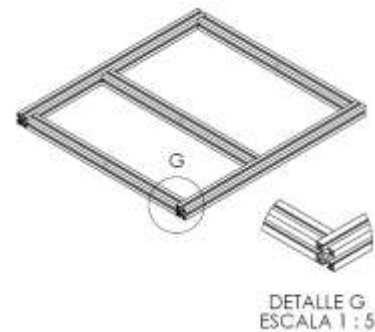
Ensamble chasis perfil Bosch. Diseño propio.
